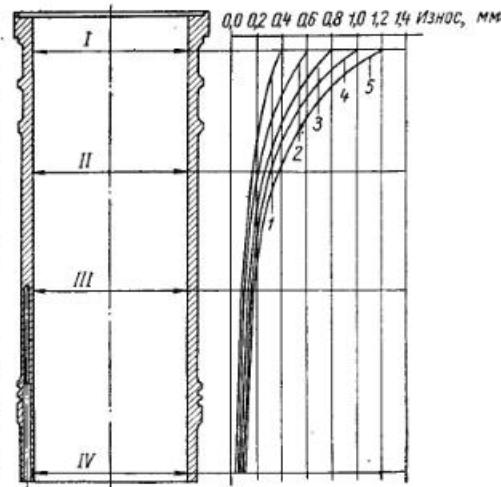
Износ (по диаметру) втулок рабочих цилиндров двигателя 6NVD-48:
